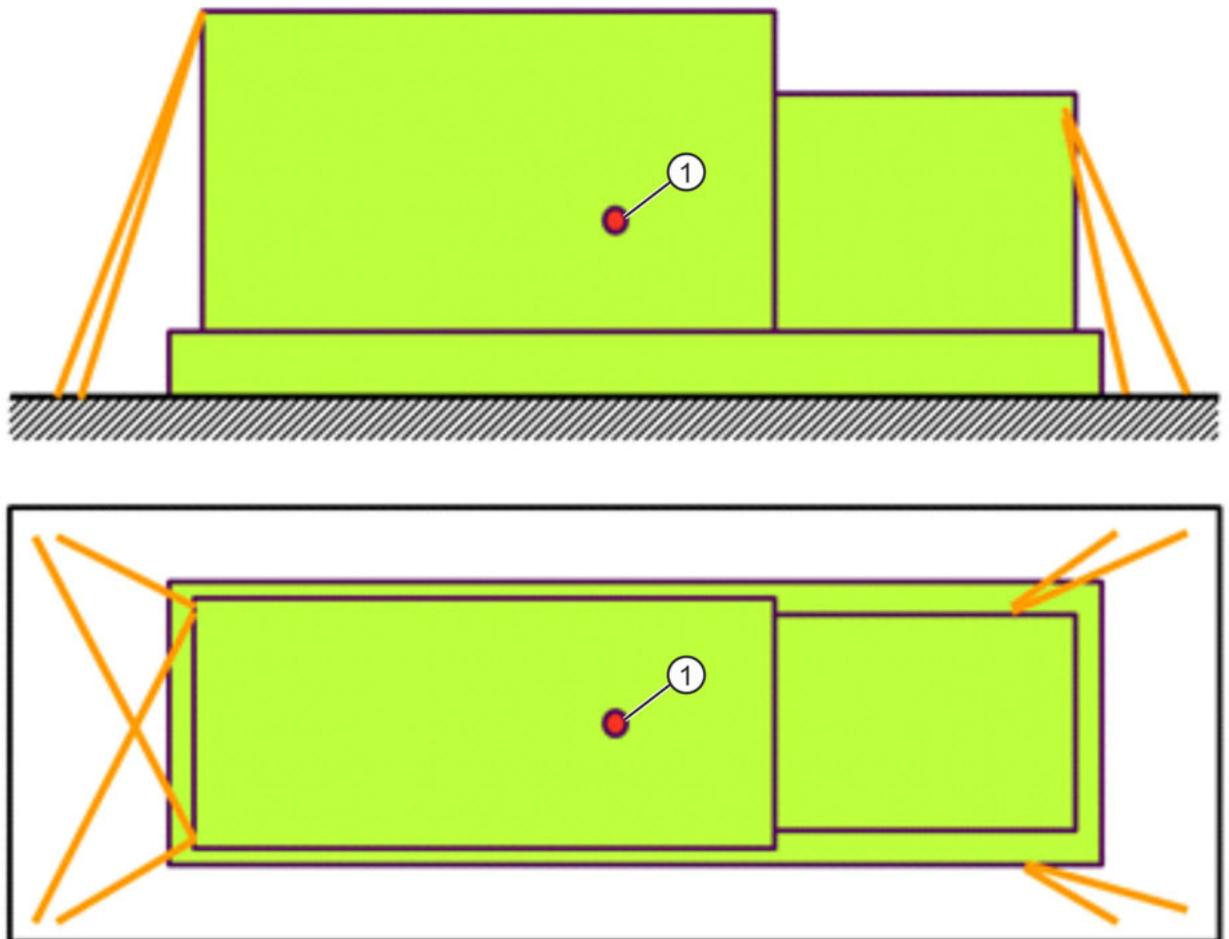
Fissaggio dei dispositivi di tensione al gruppo motore, schema, fissaggio a quattro punti
